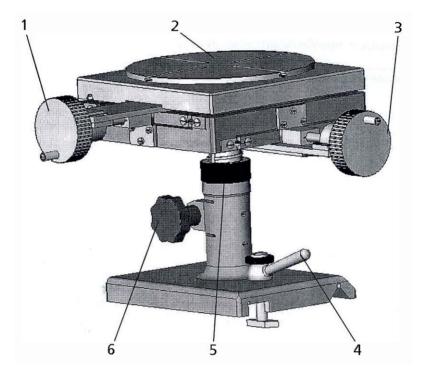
Столик двухкоординатный с преобразователями линейных перемещений
